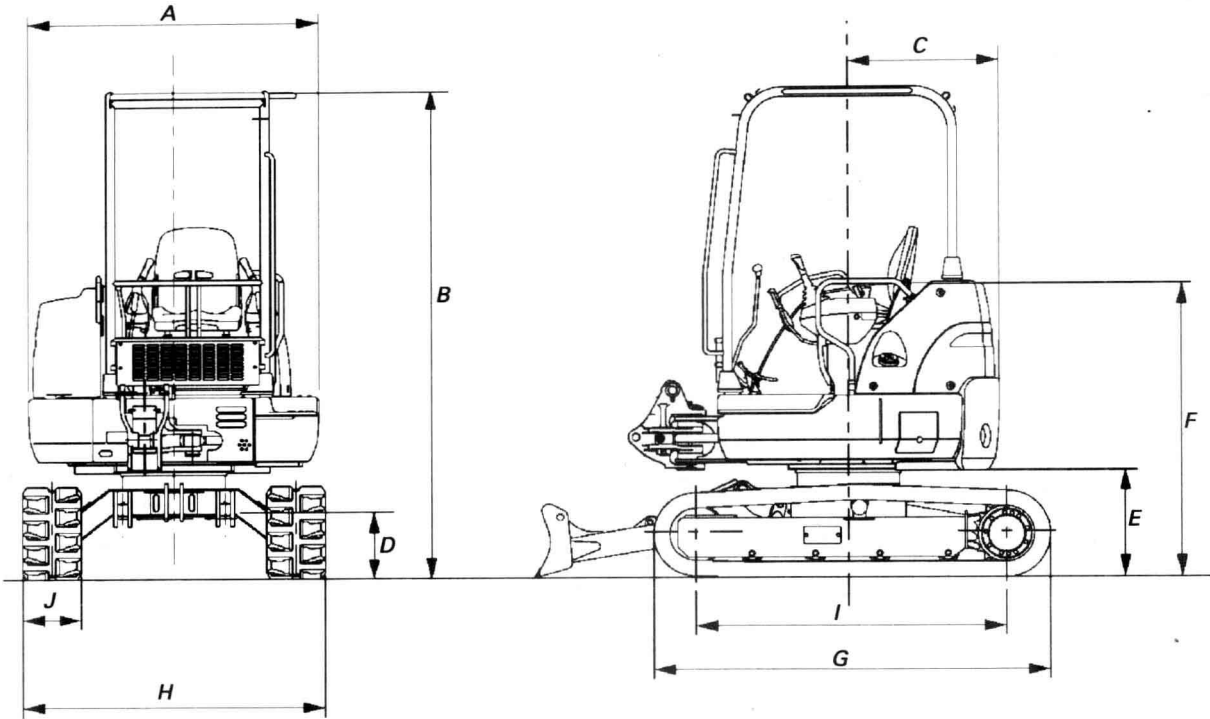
ZAXIS 350U 型挖掘机外形尺寸
